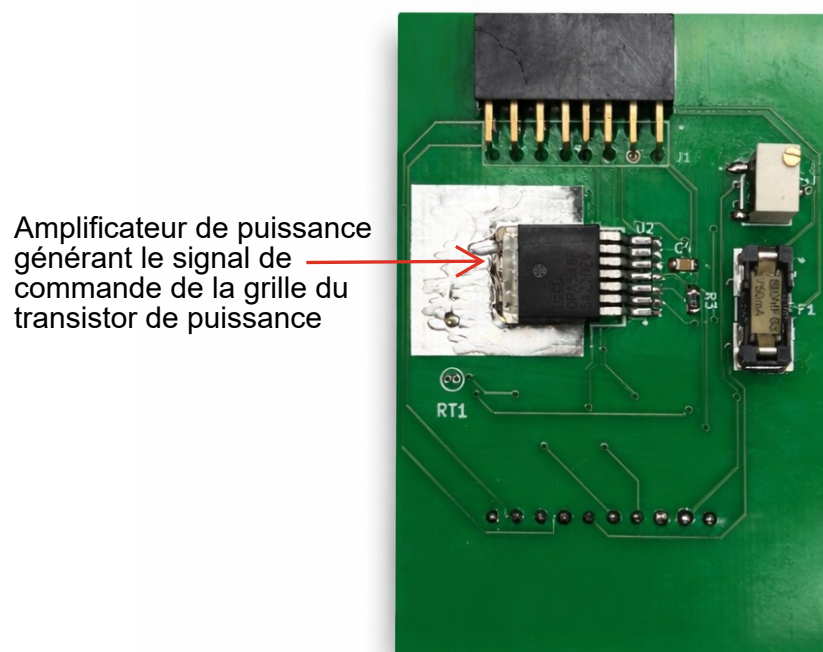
PCB de contrôle de courant – vue face 2.
